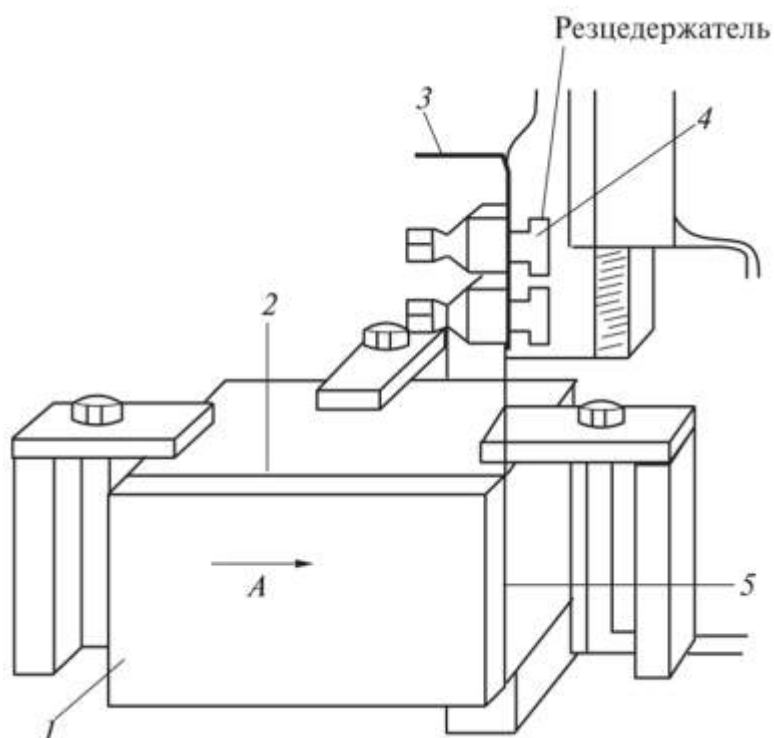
Проверка правильности расположения заготовки на столе долбежного станка
